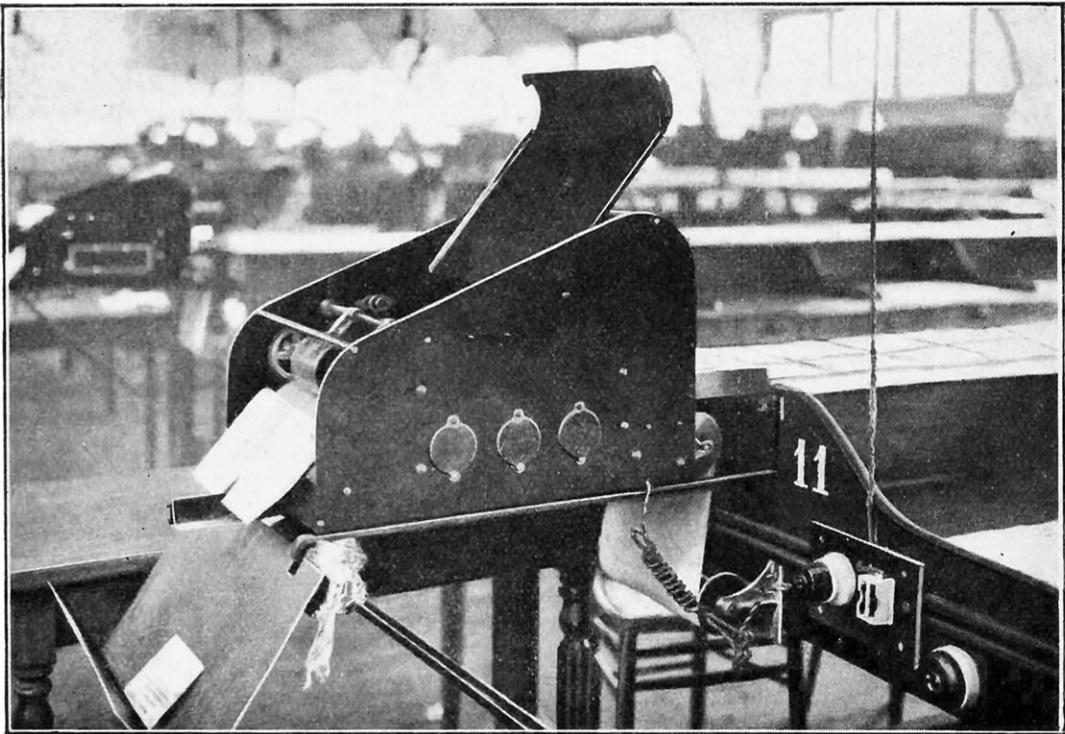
VUE GÉNÉRALE DE LA MACHINE A COLLER LES ENVELOPPES
